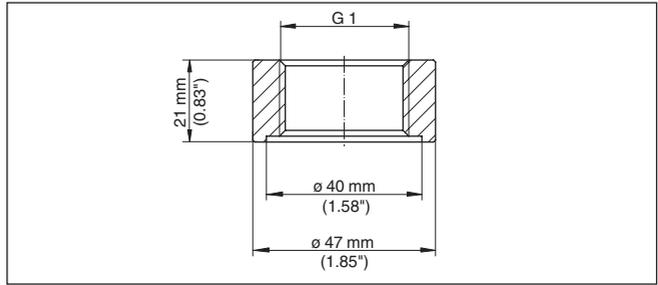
Medidas racor para soldar G1 (DIN 3852-X)
